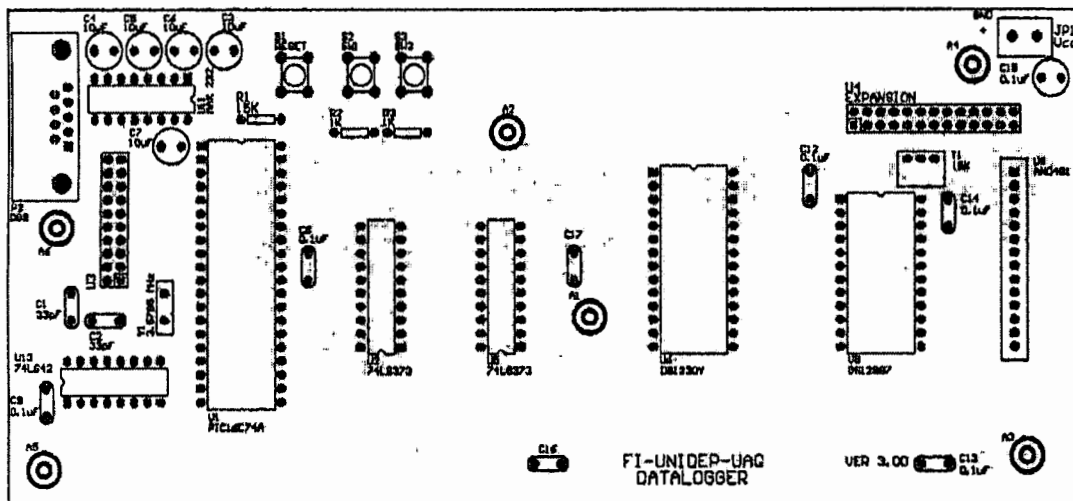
Posición de los elementos del registrador en la tarjeta impresa
